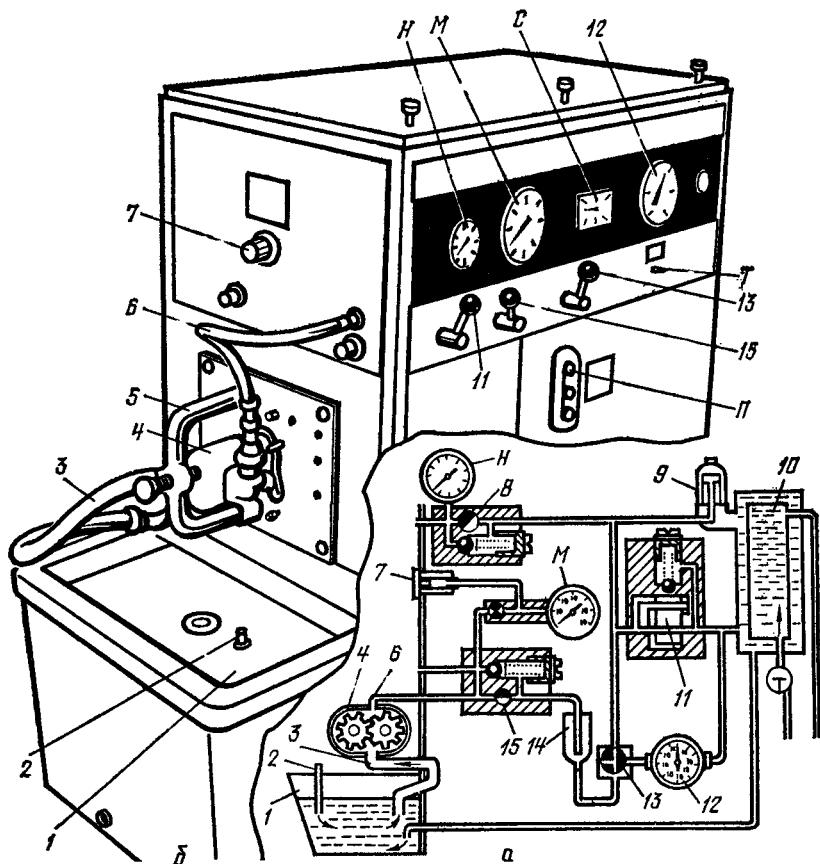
Схема присоединения насоса к гидросистеме (а) и установка его для испытания на стенде КИ-4200 (б):
